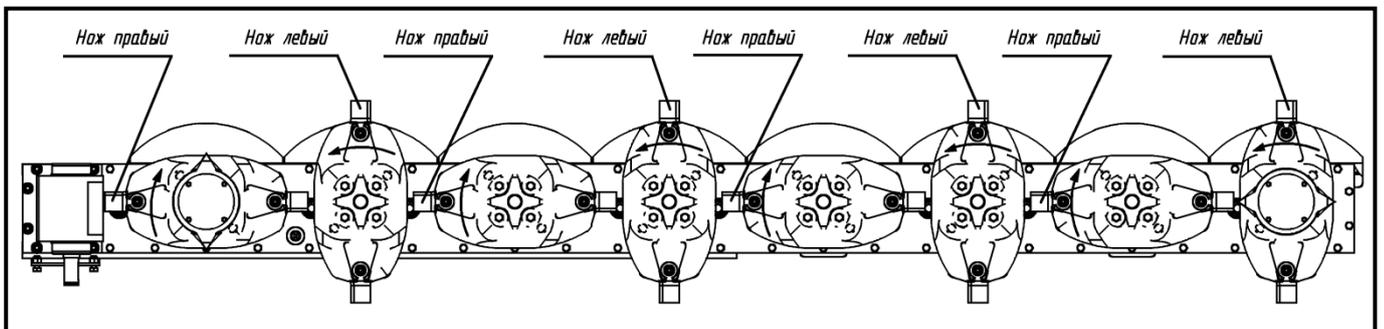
Схема установки скашивающих ножей ЖТТ-3.2
